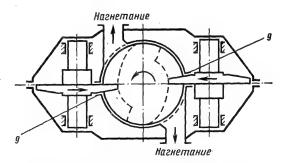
Однороторный компрессор: 1—ротор; 2— уплотнительная шестерня; 3— камера всасывания; 4— фильтр газовый; 5— корпус компрессора; 6— цилиндр; 7— окно нагнетания; 8— вал привода; 9— окно уплотнительной шестерни.
